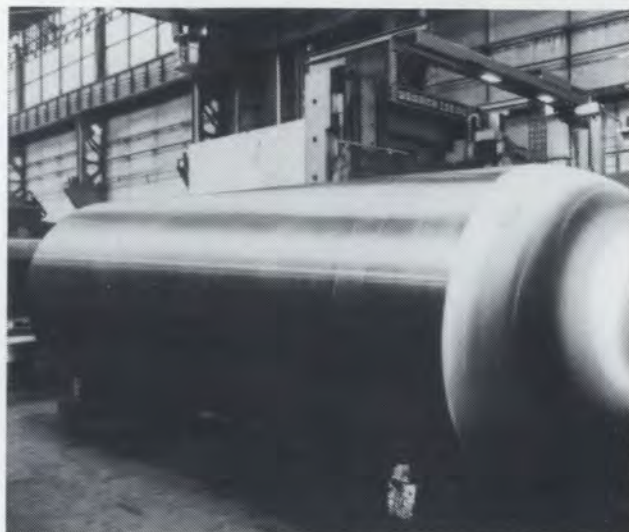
Корпус, сваренный профилированной сваркой
